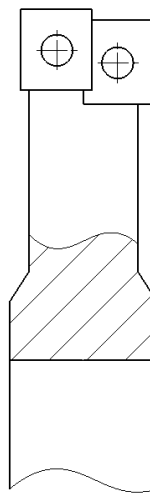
Інструмент, що працює з груповою схемою зрізання припуску
